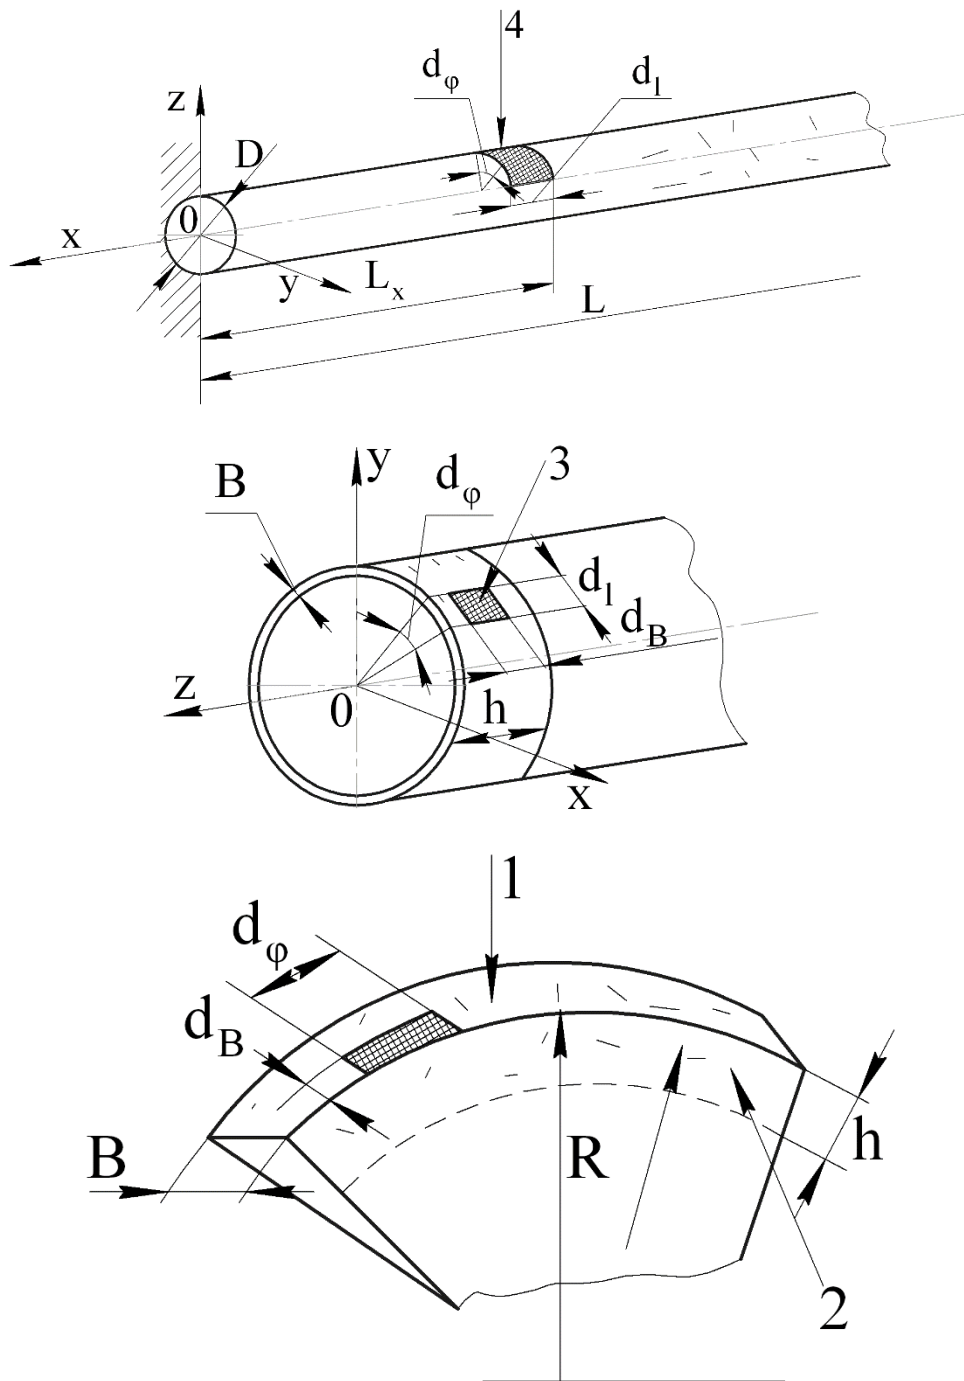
Розрахункові схеми нагріву частин поверхонь
